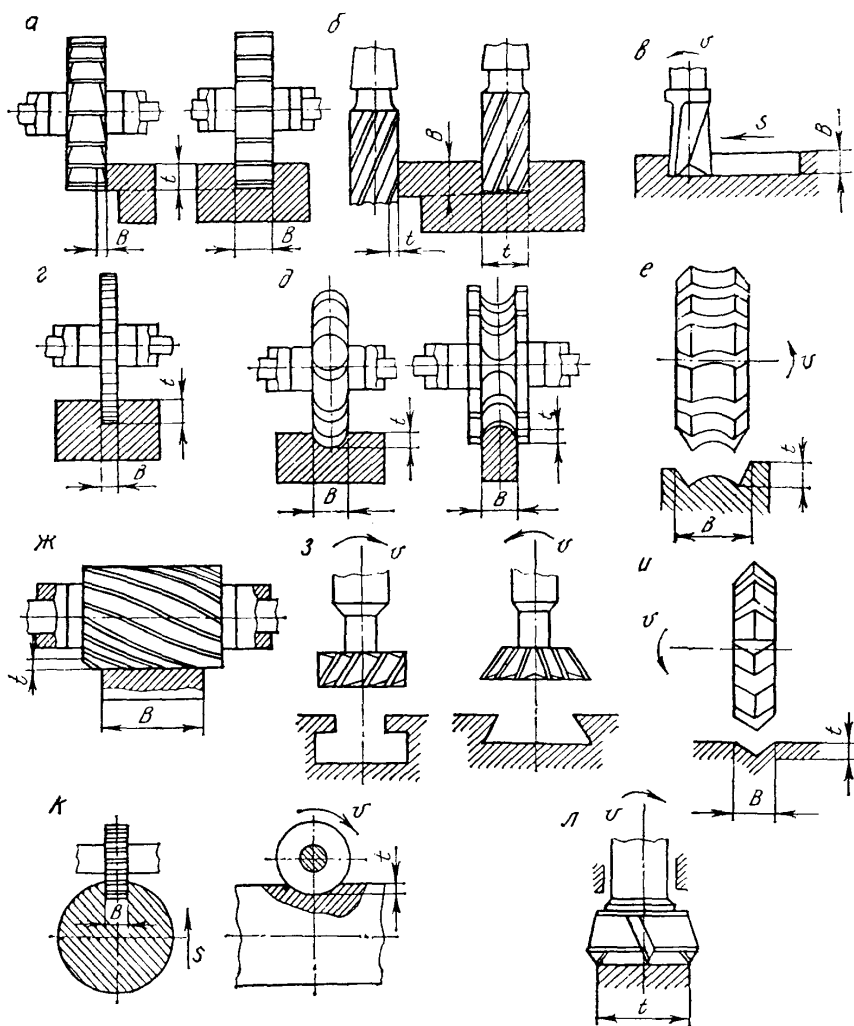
Виды работ, выполняемых на фрезерных станках
